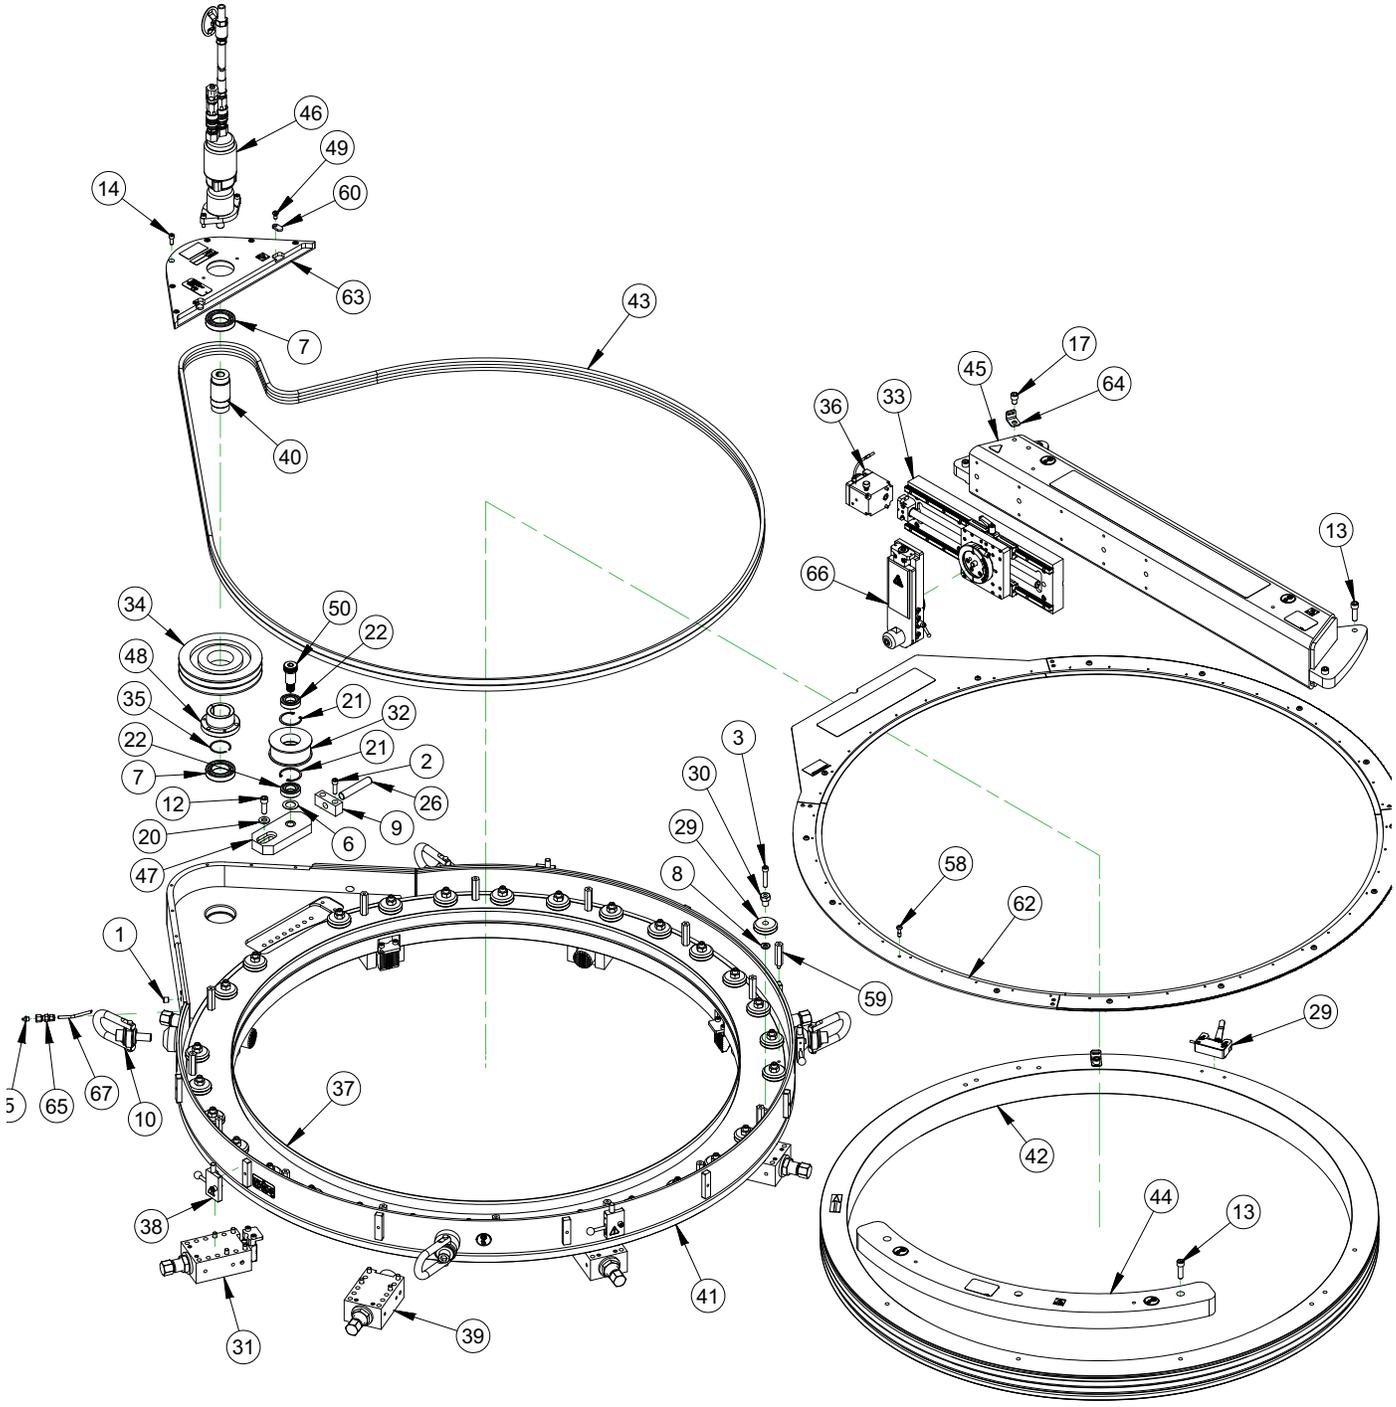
ENSEMBLE ODF50 SPEED FACER (P/N 86980)
